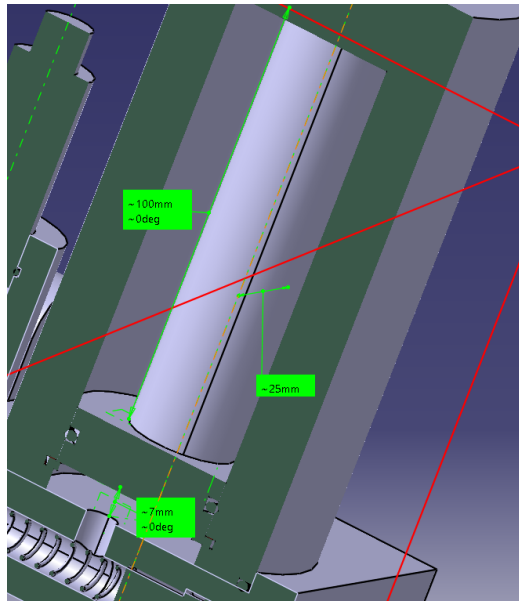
Dibujo CAD del conjunto pistón con medidas
